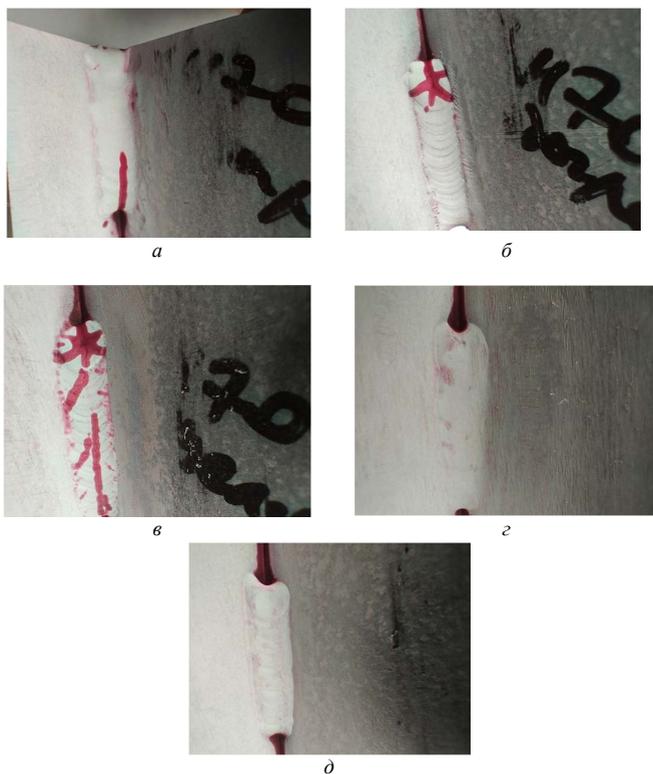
Капиллярный контроль сварных образцов:
